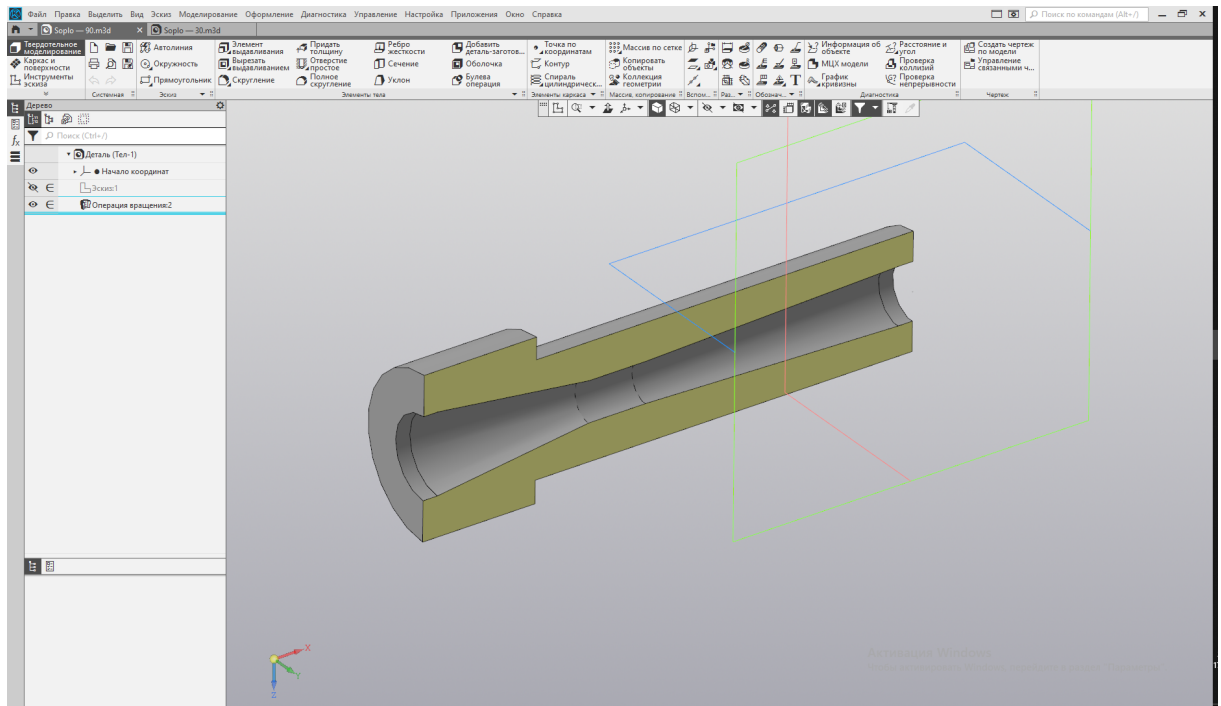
Компас 3D – 3D-модель обрабатывающего сопла
